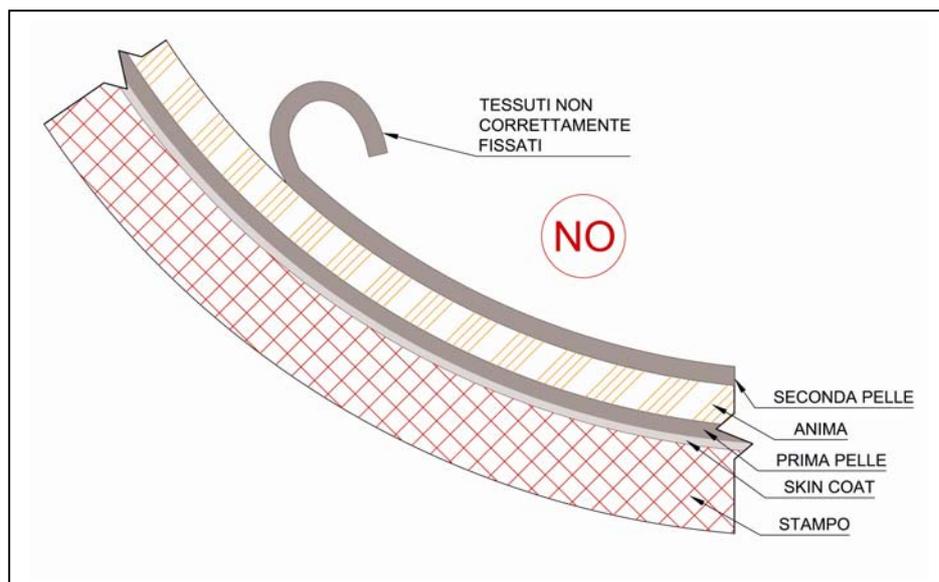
TESSUTI NON CORRETTAMENTE FISSATI
